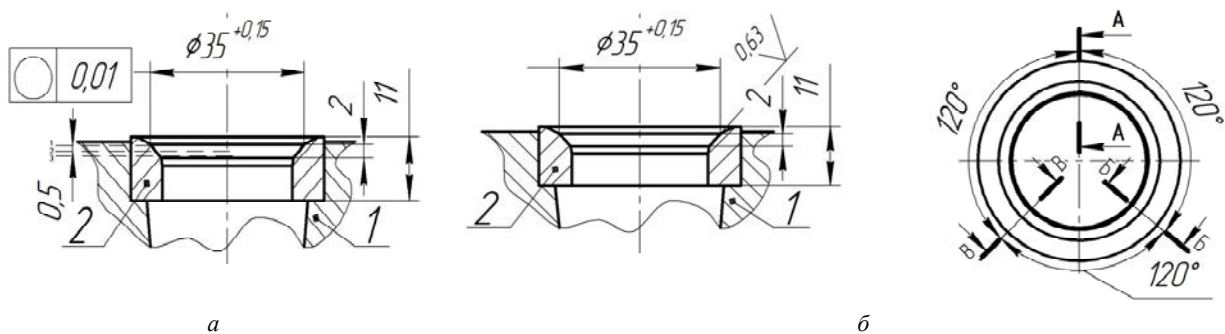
Схемы расположения сечений при измерении: (а) - отклонения от круглости обработанной поверхности сѐдла клапана; (б) - шероховатости обработанной поверхности; 1 – головка блока двигателя; 2 – сѐдло клапана
